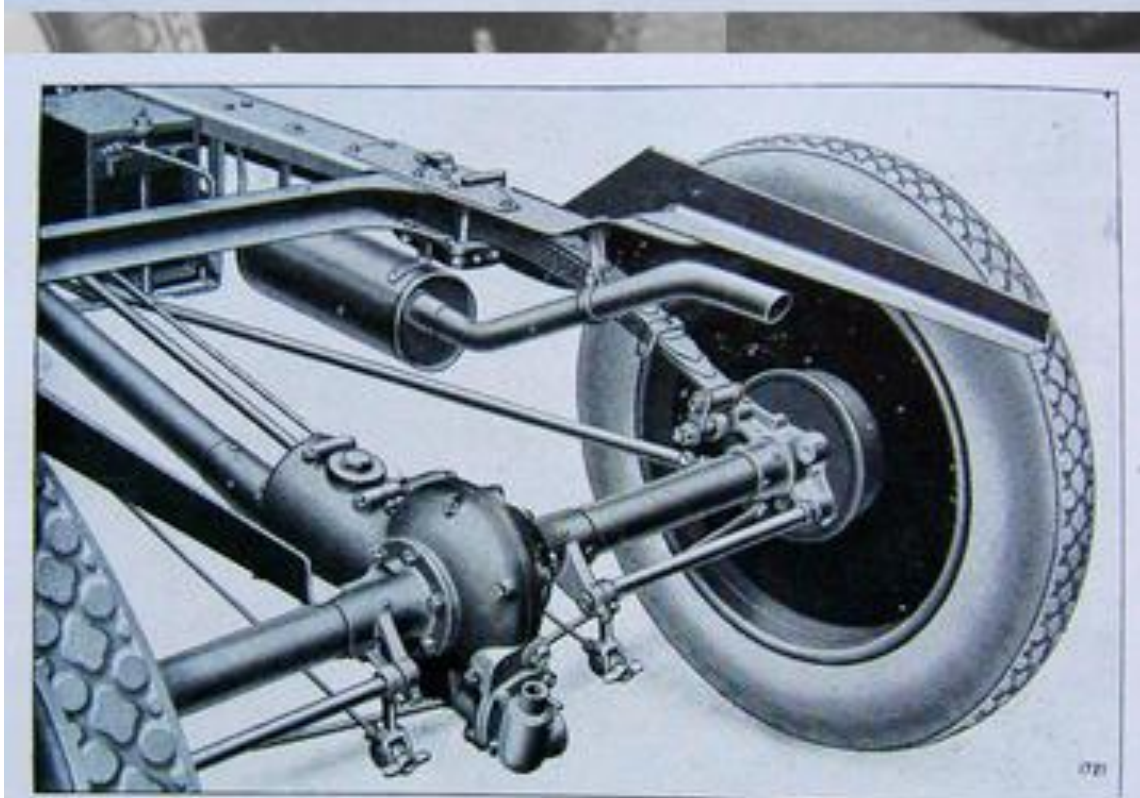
BOITE DE VITESSE ET ESSIEU ARRIÈRE.
